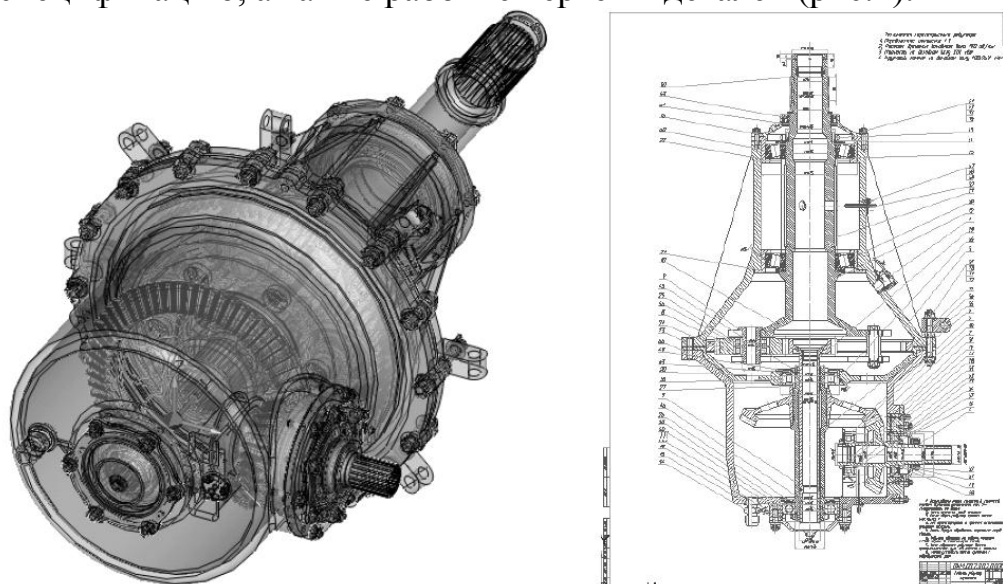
3D-модель редуктора в сборе и созданный на её основе сборочный чертёж
